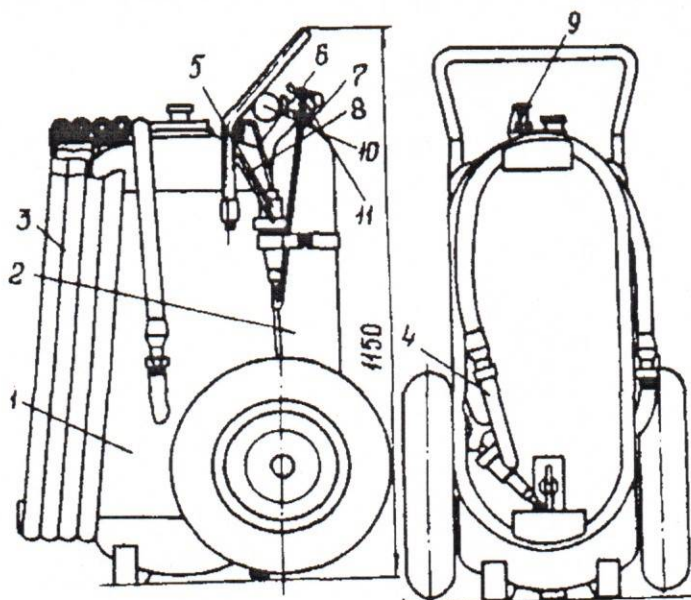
Общий вид передвижного порошкового огнетушителя ОП-100:
